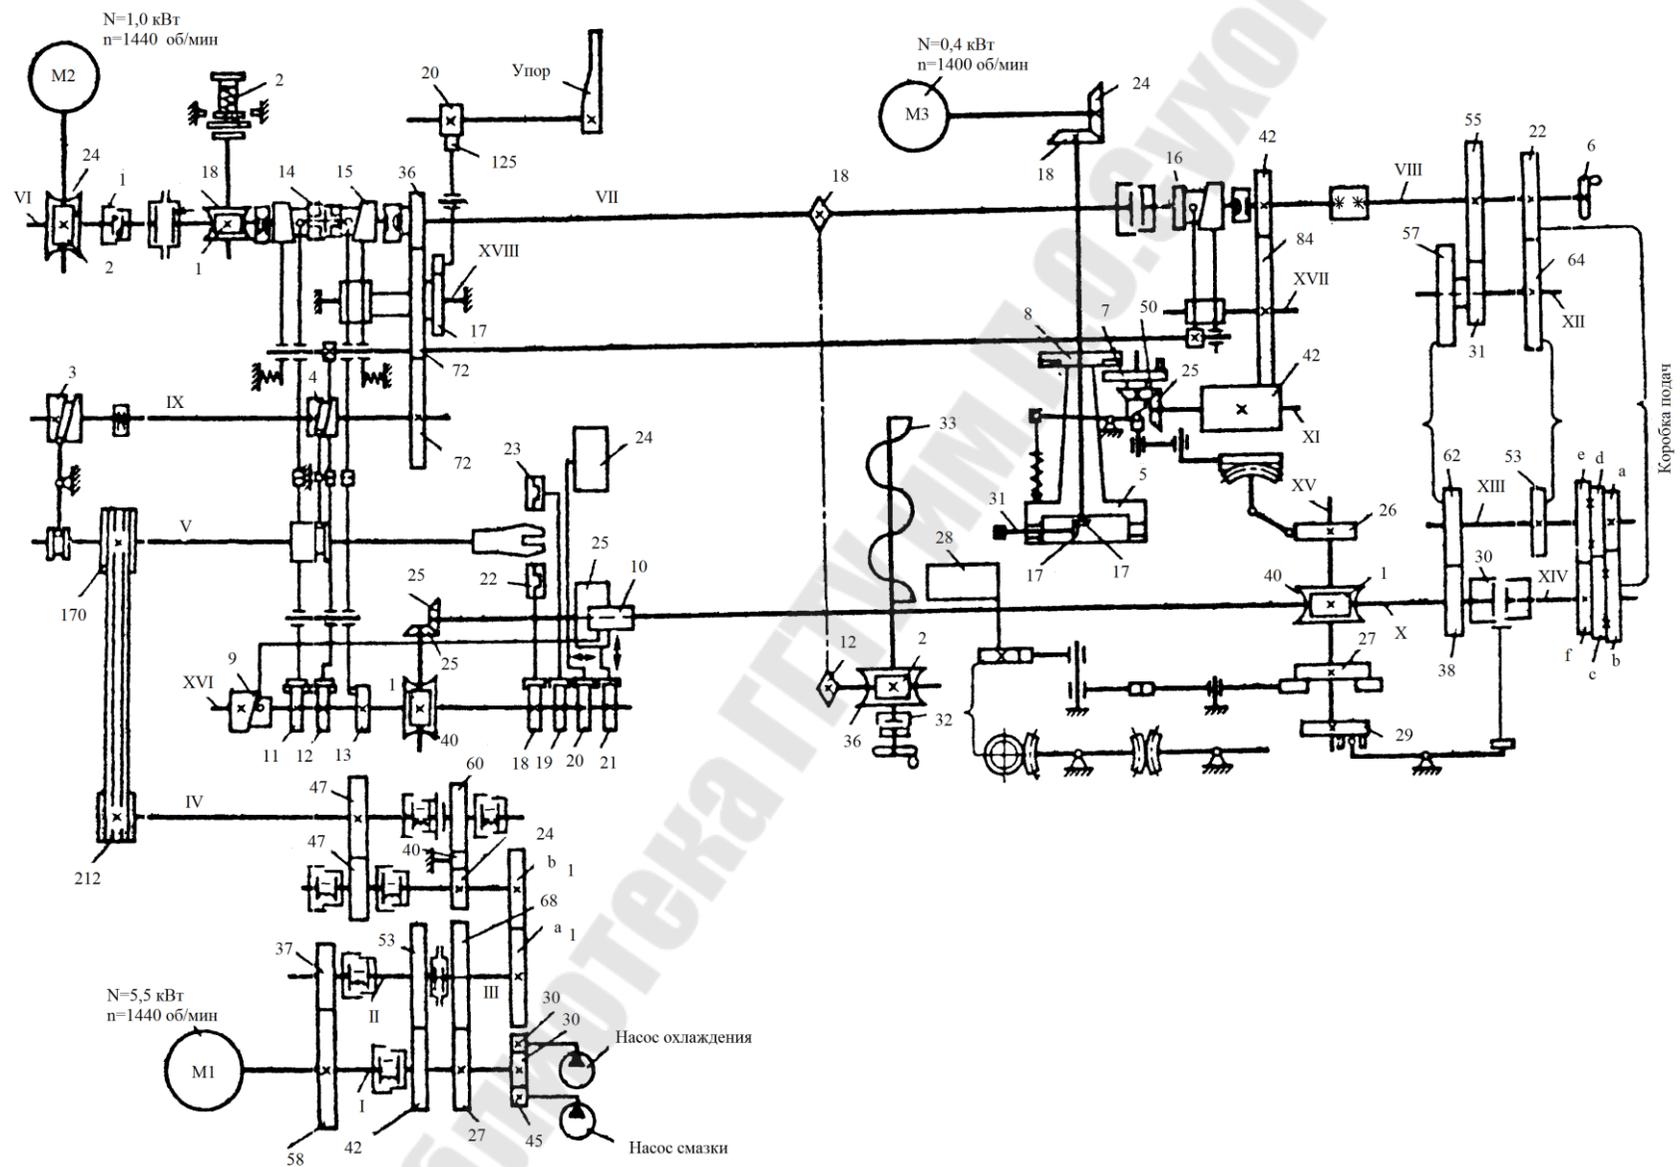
Кинематическая схема токарно-револьверного одношпиндельного автомата
